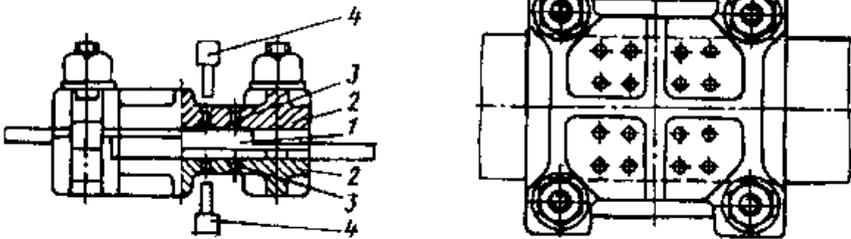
Схема сварки с предварительным зажатием свариваемых деталей в кондукторе.
